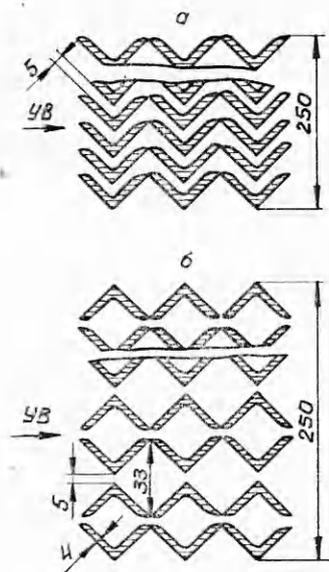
Сечения перфорированной (а) и железобетонной (б) испытательных камер.
